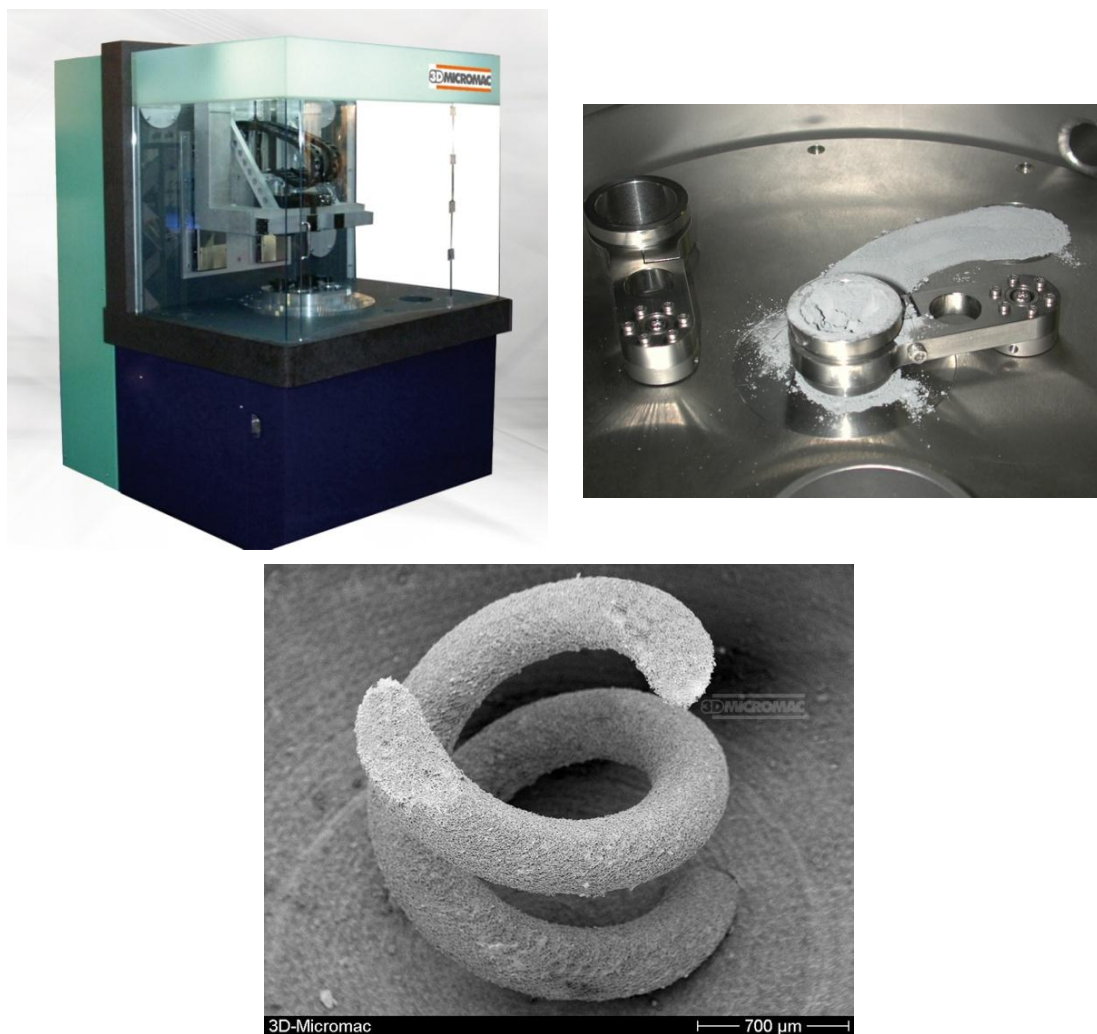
Image de la machine SLM MicroFORM et exemple de pièce
